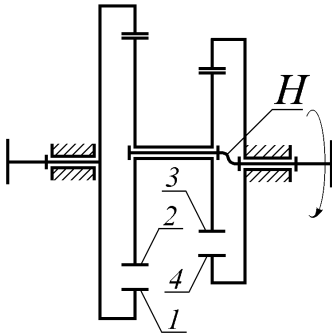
Схема планетарного редуктора Давида з двома внутрішніми зачепленнями
